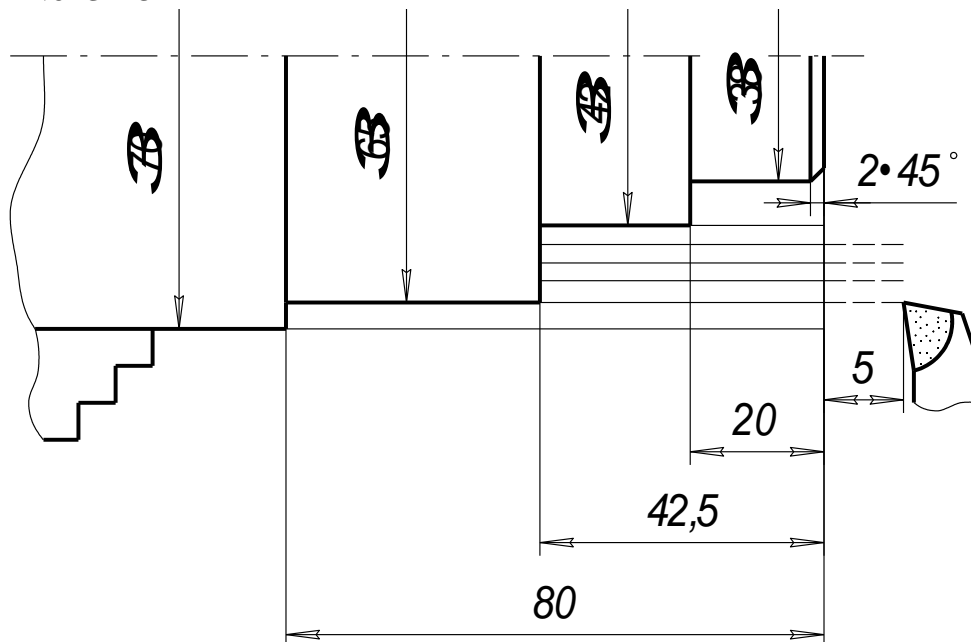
Схема обробки циліндричних ступінчатих поверхонь
